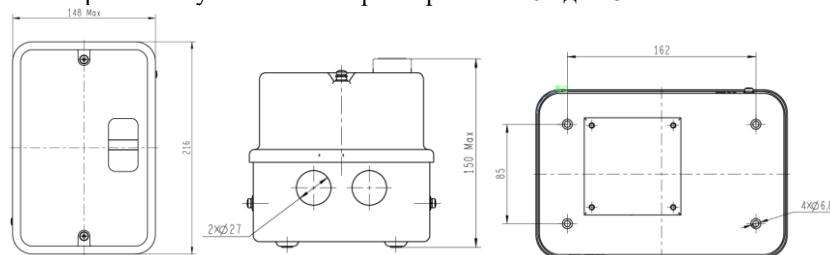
Габаритные и установочные размеры ПМ-102 25-38А в металлическом корпусе
